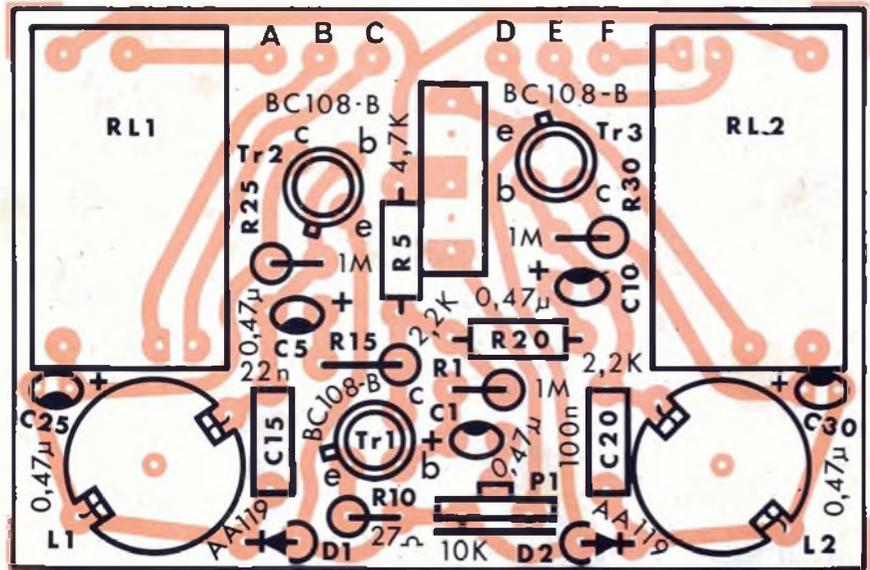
Montaggio dei componenti sulla basetta a circuito stampato dell'UK 325/A.
